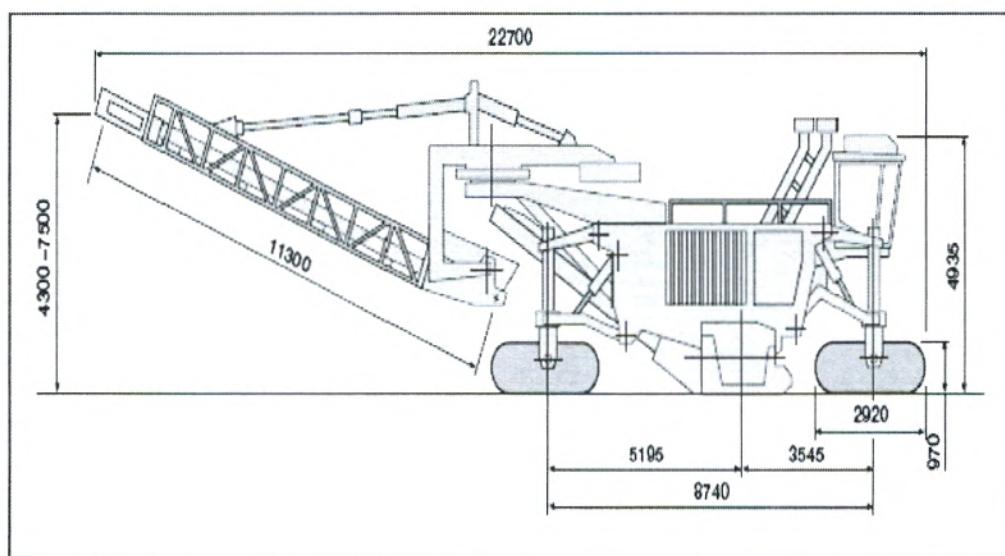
dimensions en millimètres des constituants du Surface Miner type 2500 SM
